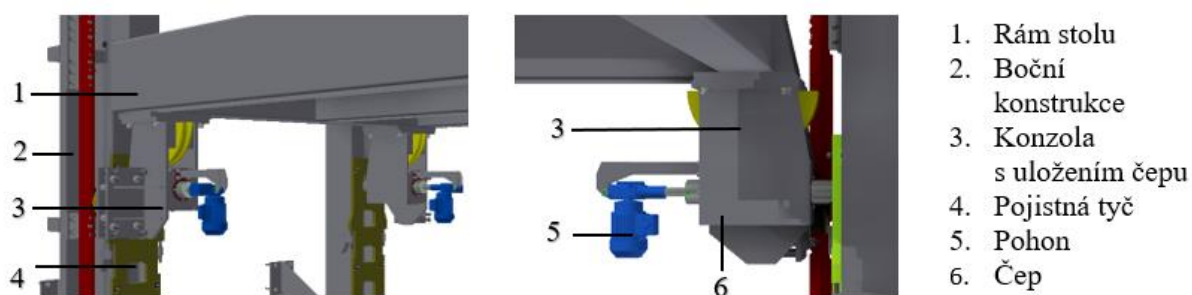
Jištění polohy pomocí klešťového mechanismu [2]
